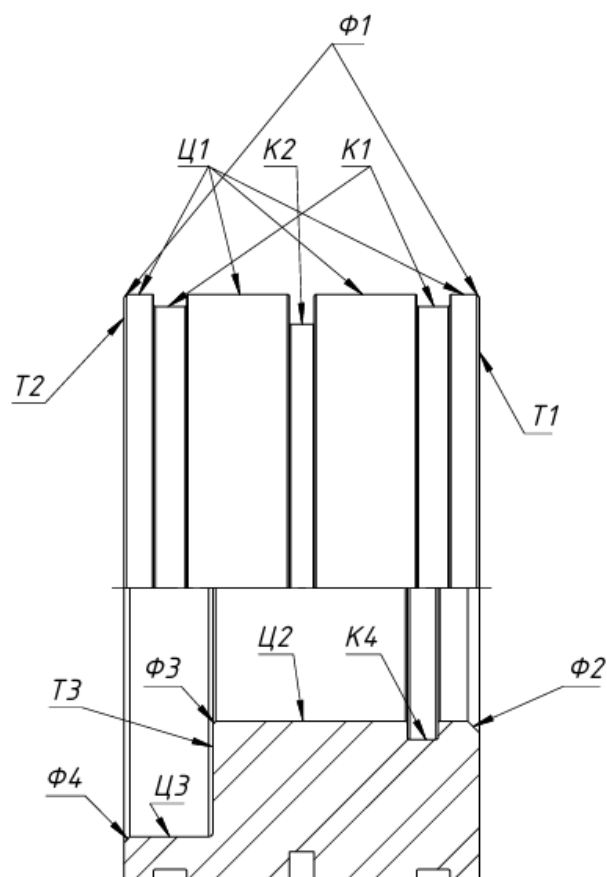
Нумерація поверхонь деталі «Поршень»
